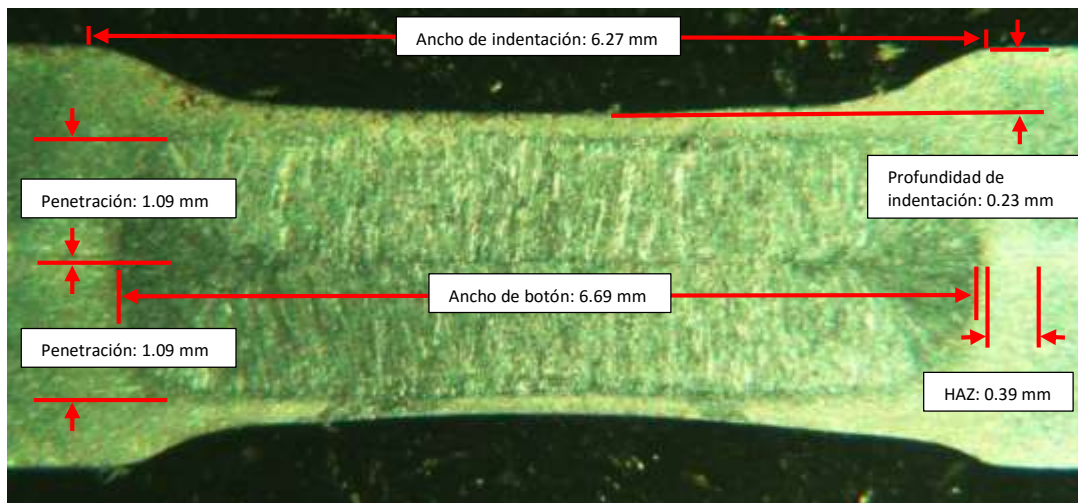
Mediciones realizadas en el botón de soldadura número 12.
